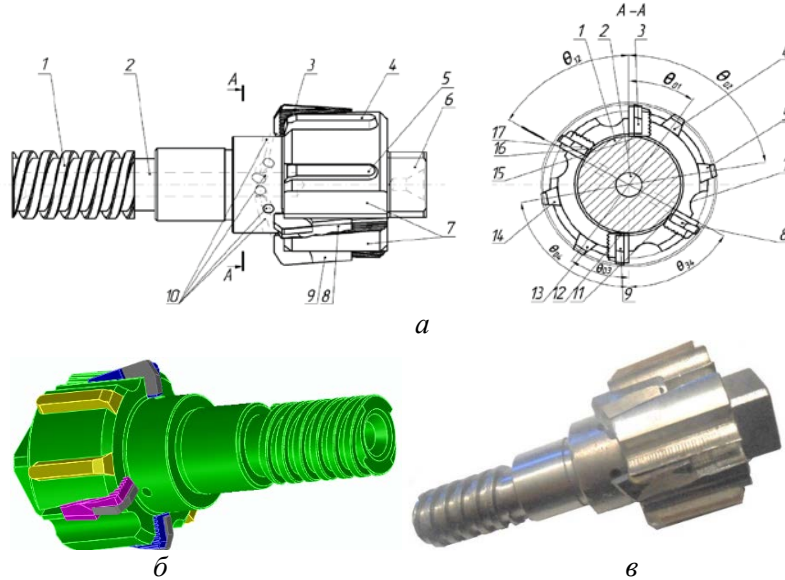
Конструкція розточувального інструменту з попарно-асиметричним розміщенням лез: а – конструктивна схема; б – 3-D модель; в – фотографія
